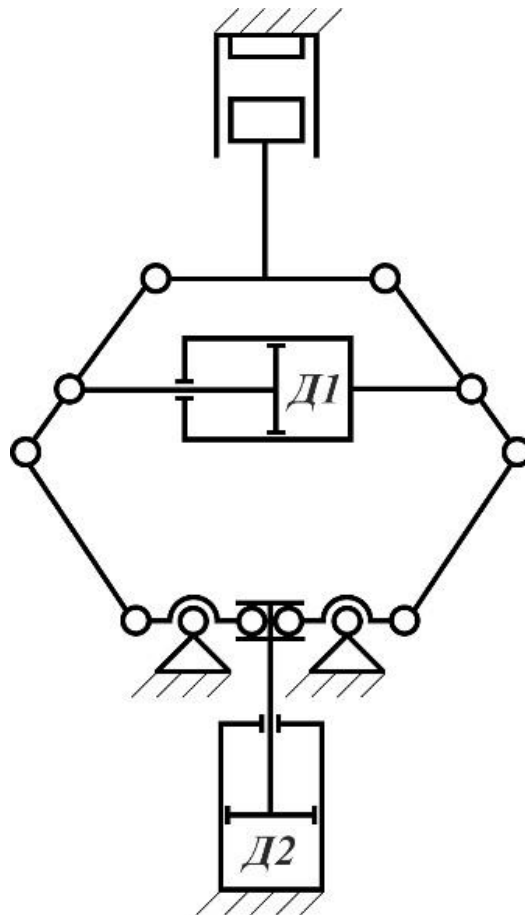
б. Кинематическая схема двухпоточного механизма силовой станции с двумя приводами, размещенными на неподвижном основании.
